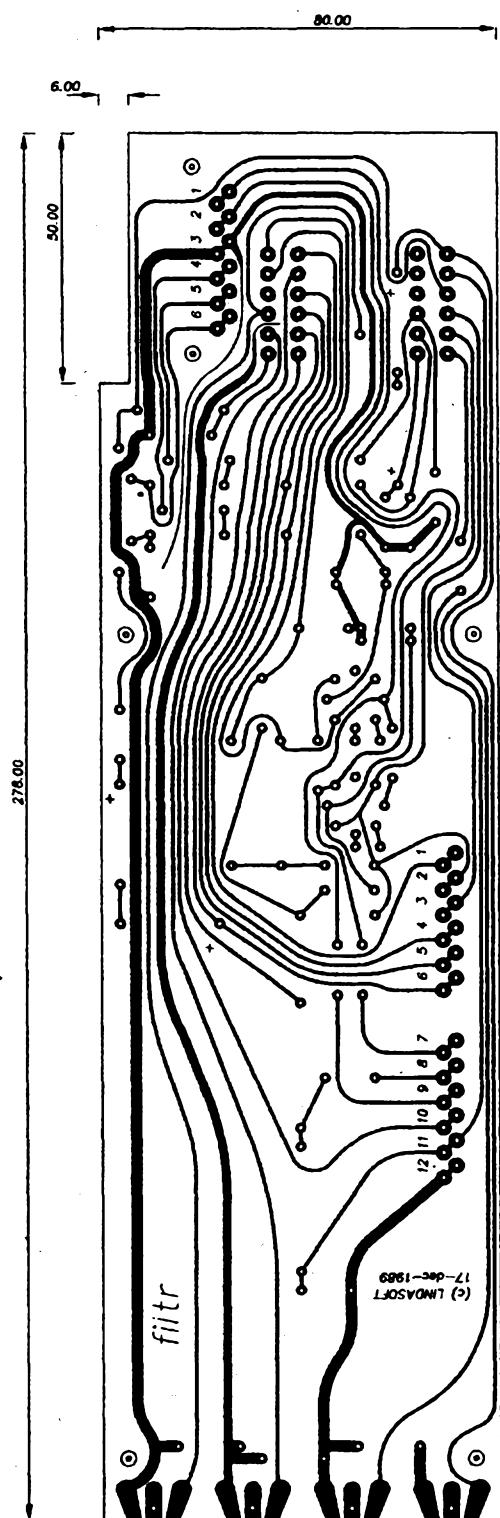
Obrazec plošných spojů procesoru (deska Z22)
